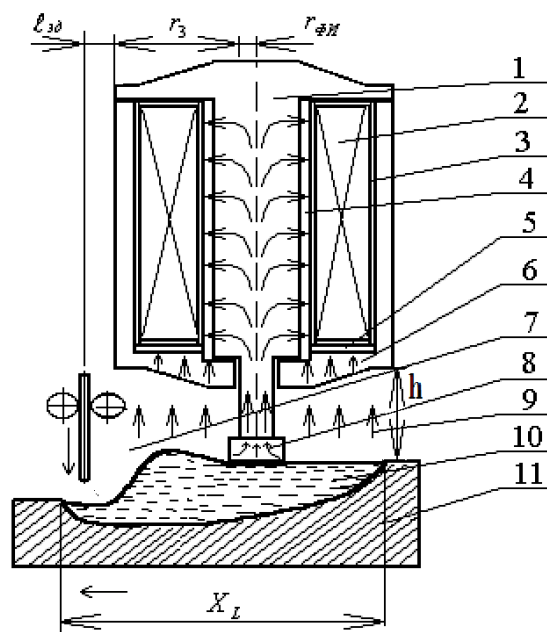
Схема размещения ЛЭМД относительно наплавочной ванны (1 - якорь, 2 - обмотка, 3 - изоляция обмотки, 4 - воздушный промежуток, 5 - прокладка из плотной бумаги, 6 - нижняя дисковая часть, 7 - сварочная дуга, 8 - пуансон, 9 - потоки тепла, 10 - наплавочная ванна, 11 - наплавляемая деталь)
